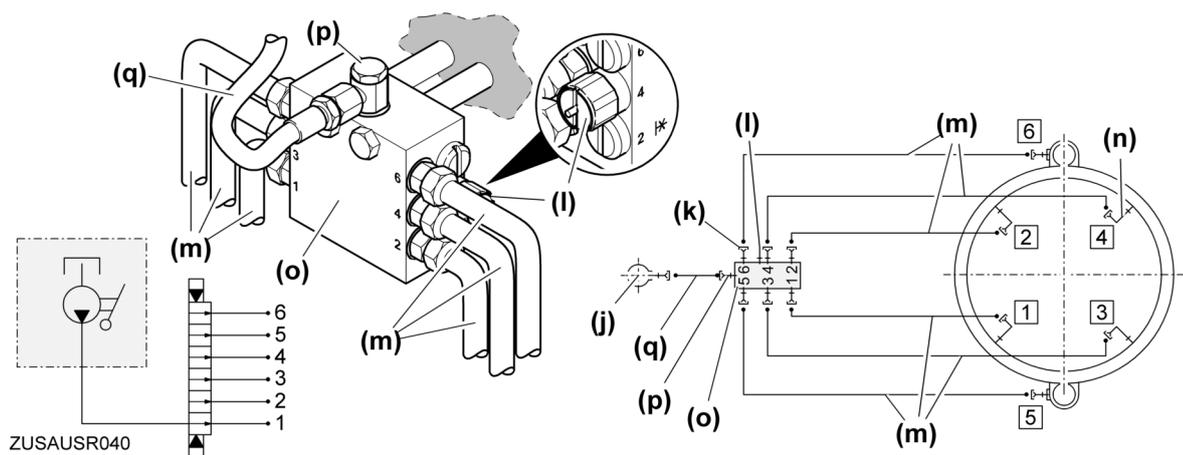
Verlegeplan und Hydraulik-Schaltplan (6er-Verteiler mit 2 Drehwerken)
